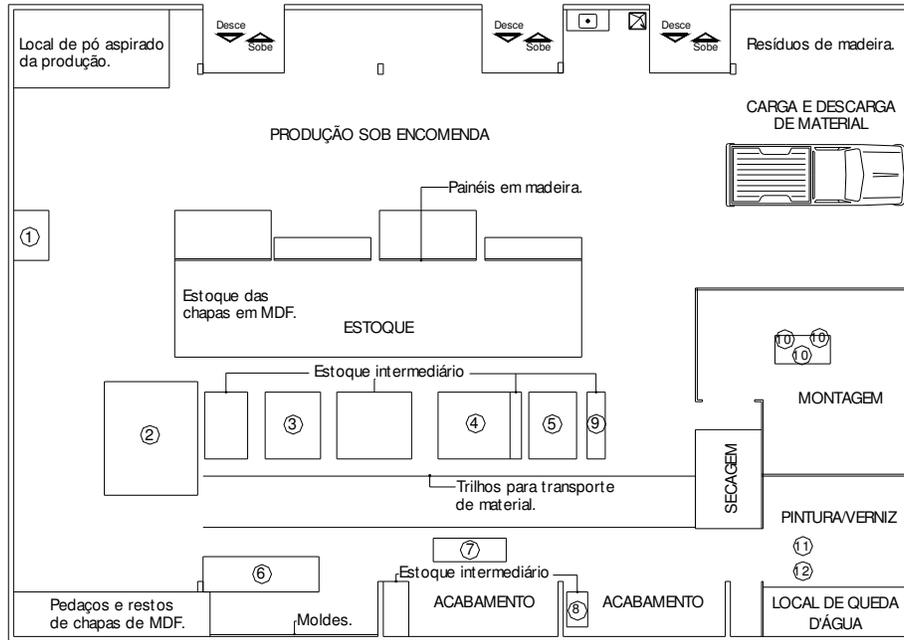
Planta baixa 5: Galpão 3 com lay-out antigo com a linha de produtos sob encomenda. (Equipe de Projeto).
